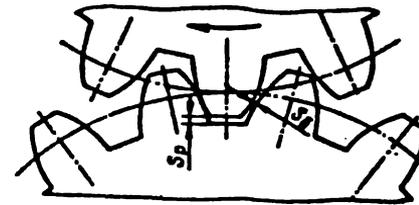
Радиальный и боковой зазоры зубчатого зацепления
